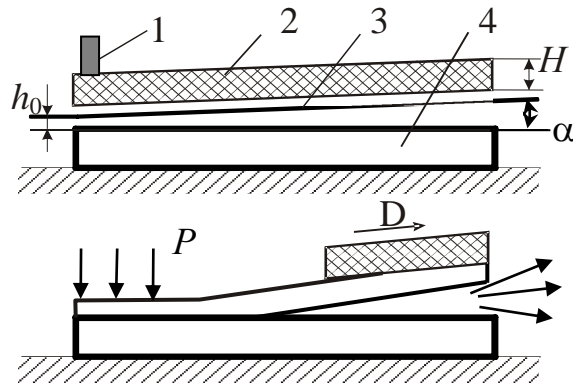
Принципова схема зварювання вибухом: 1 – детонатор; 2 – вибухова речовина; 3 і 4 – заготовка (пластини)
